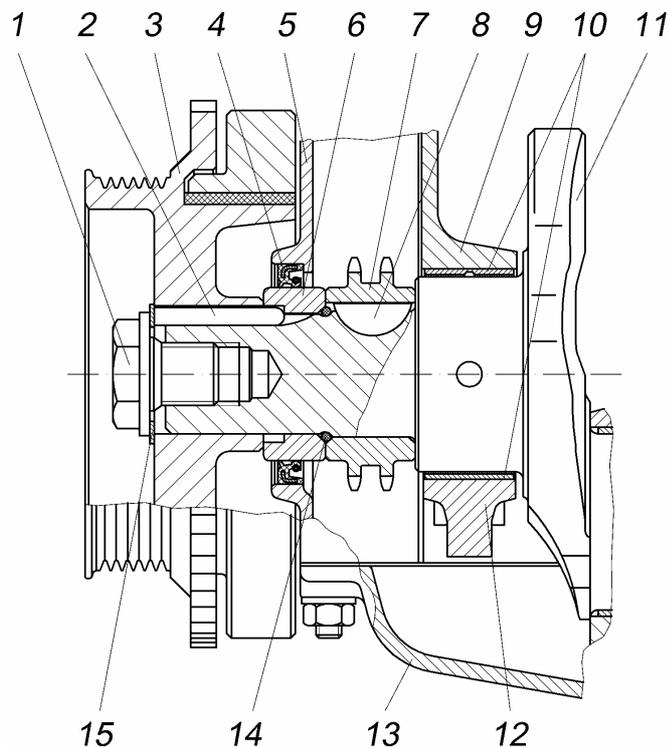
Передний конец коленчатого вала с одноручьевым шкивом:
